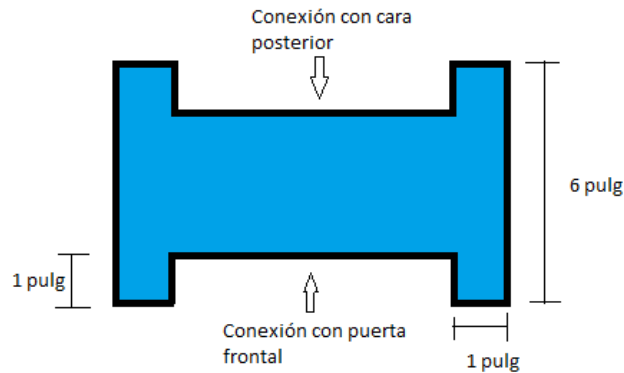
Dimensiones para las caras superior y base del cooler. *Fuente: Propia.
